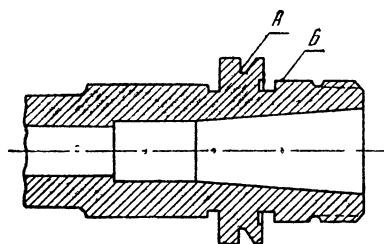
Передняя часть шпинделя токарно-винторезного станка: а — канавка для стопорного винта; б — центрирующий пояс.
